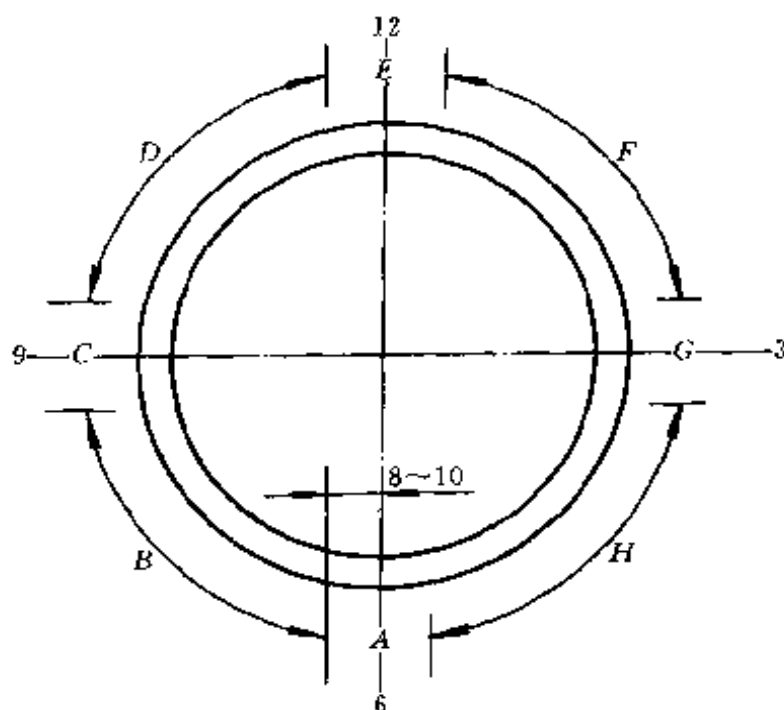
小管水平固定对接焊缝的时钟位置图
